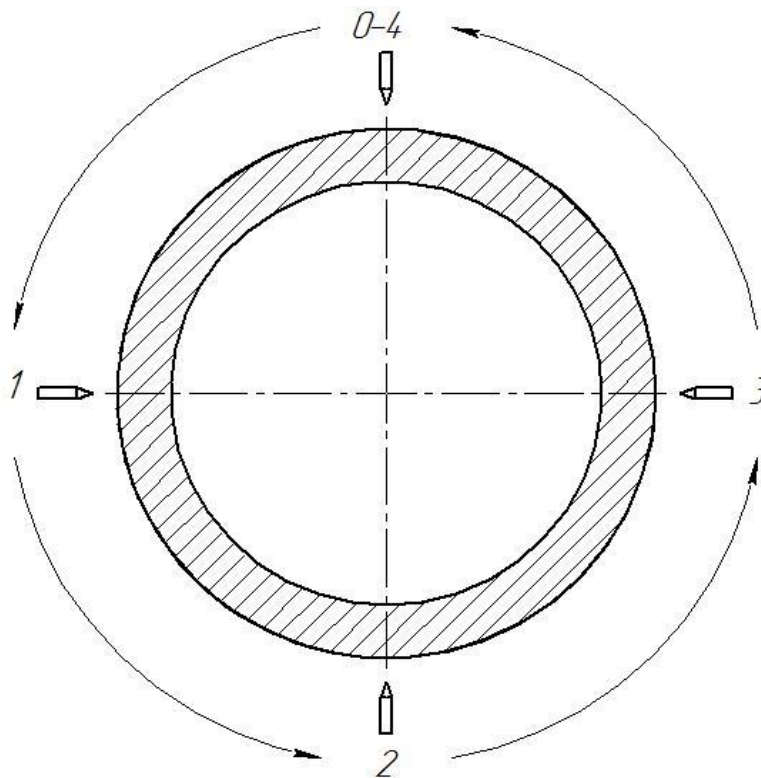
Схема сварки неповоротного стыка
